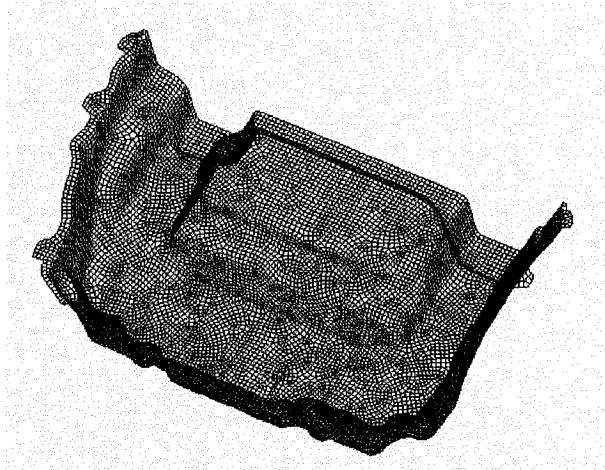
Pièce arrière remaillée pour les besoins du drapage.
